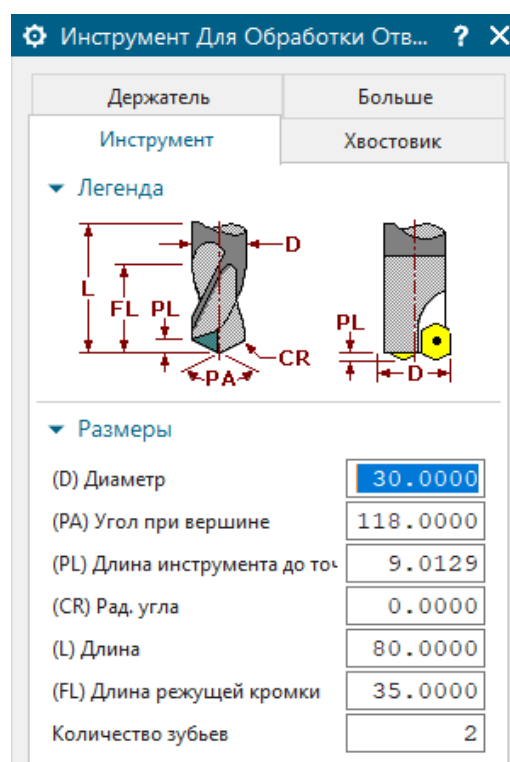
Налаштування ріжучого інструмента для переходу №2 – свердло Ø30
